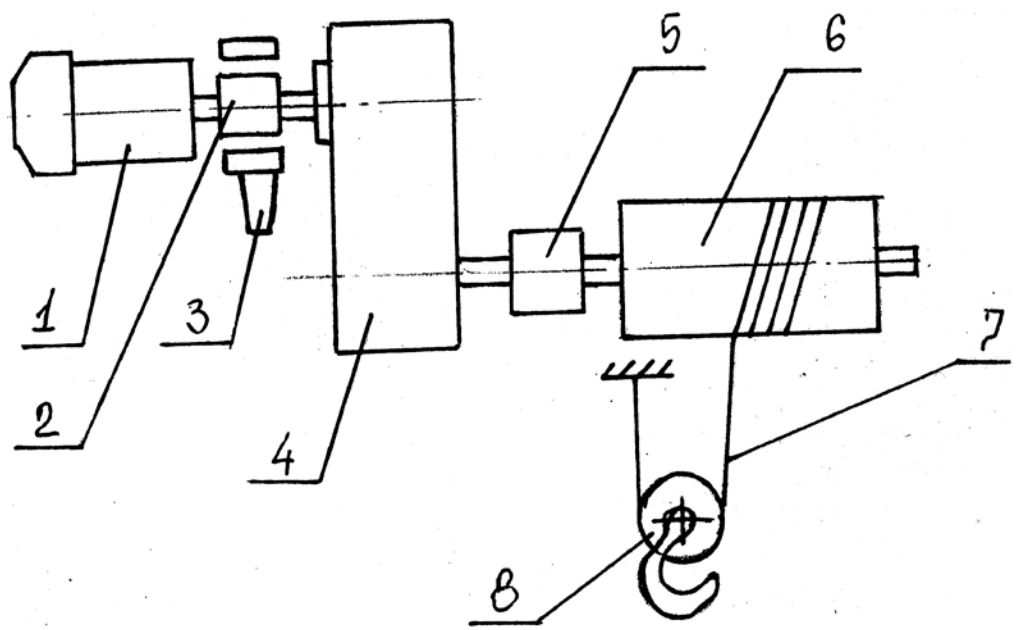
Структурная схема механизма: 1–электродвигатель; 2–муфта; 3–тормоз; 4–редуктор; 5–барабан; 6–крюковая подвеска; 7–полиспаст (тяговый орган); 8–крюковая подвеска.
